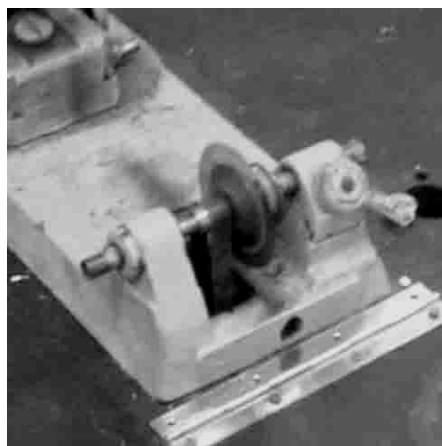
Шпиндельный узел станка мод. ШП-2
